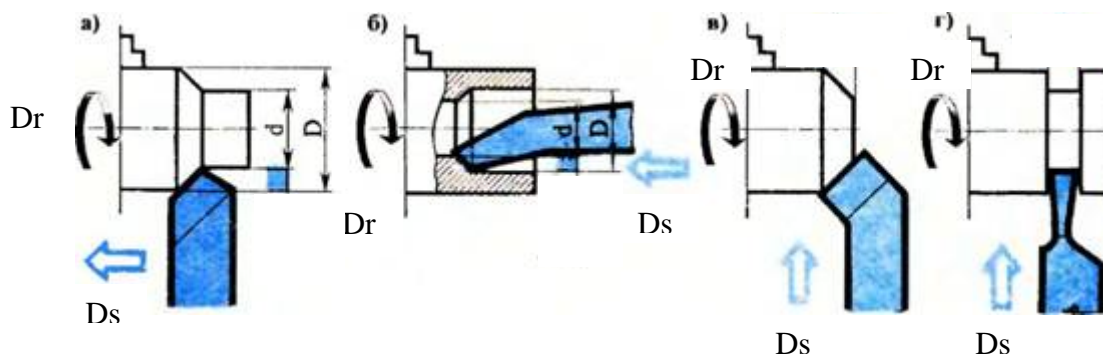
Схемы обработки поверхностей заготовки точением:
